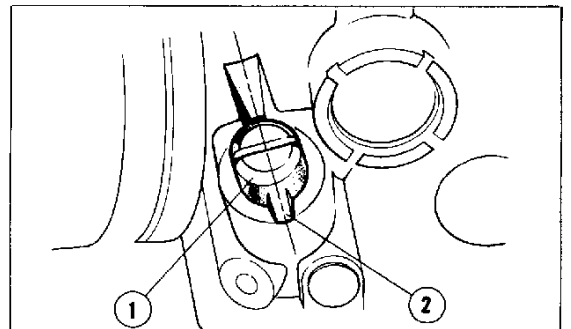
(1) Anschlagkappe der Gemischregulierschraube
